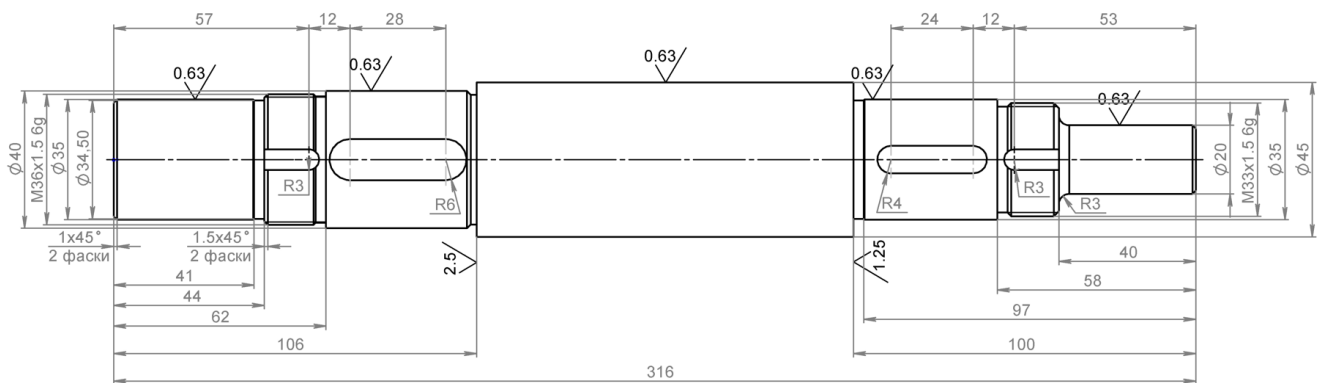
Деталь «Вал МР ПМ 629.00.002/24»
